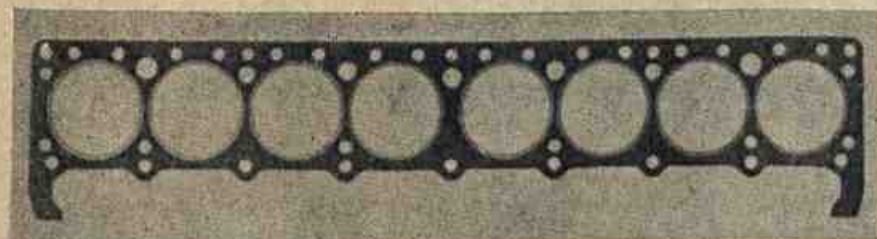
Gaxeta de aço da cabeça do cilindro, usada num motor de 8 cilindros de válvulas elevadas.
